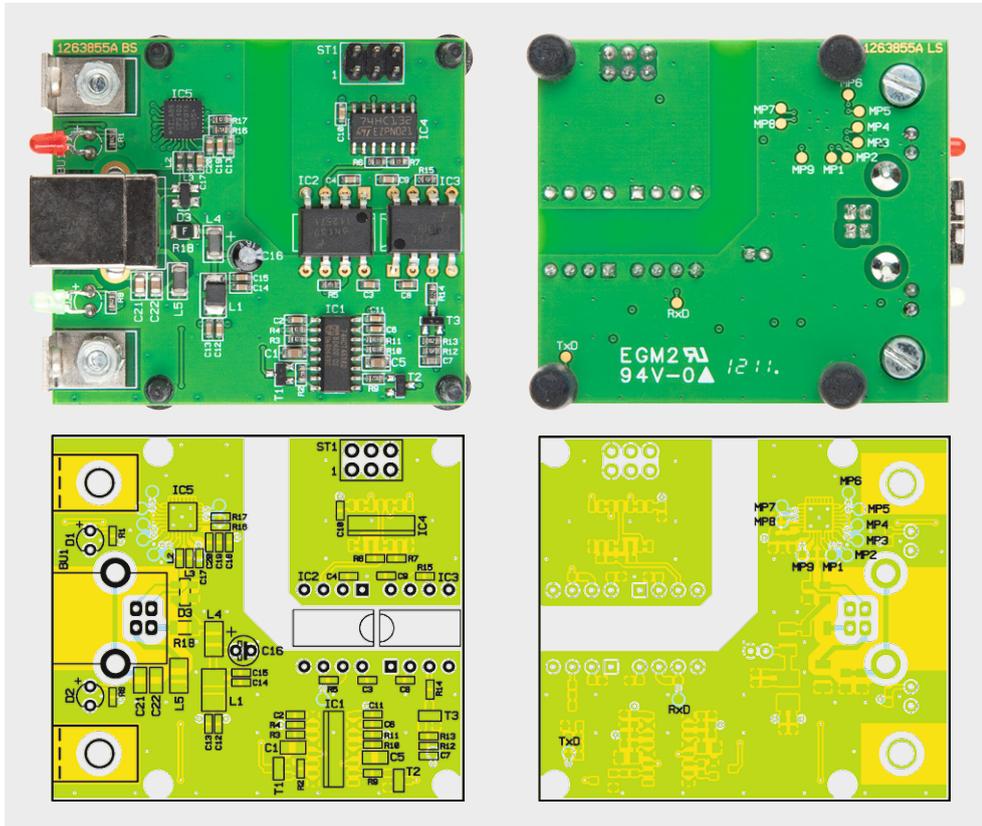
Die komplett bestückte Platine des U02102 mit dem zugehörigen Bestückungsplan. Hier ist das Modul sowohl mit den Befestigungswinkeln als auch mit den Gummifüßen bestückt.
